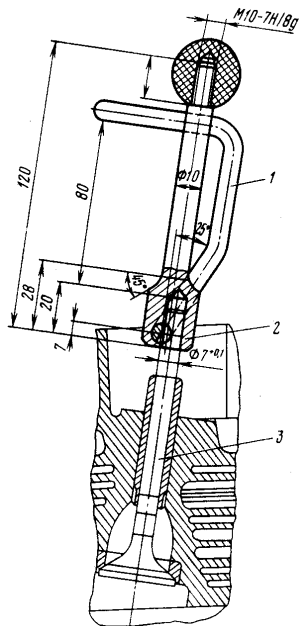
Приспособление для притирки клапанов : 1 - зажим; 2 — оправка; 3 — клапан
